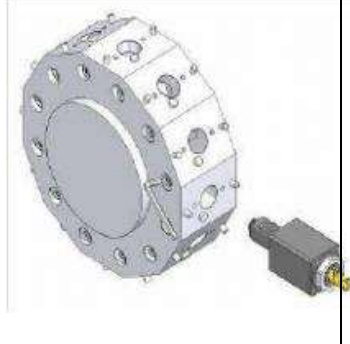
Револьверна головка ВМТ з блоками приводного інструмента[3]
